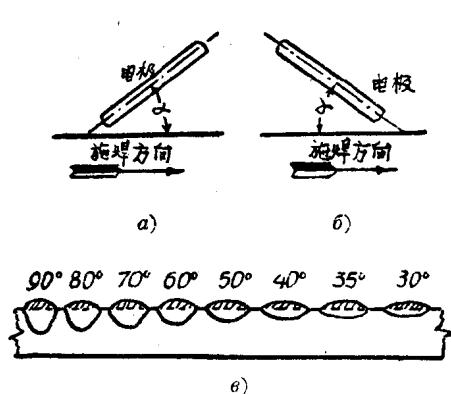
焊丝倾斜对焊缝成型的影响
